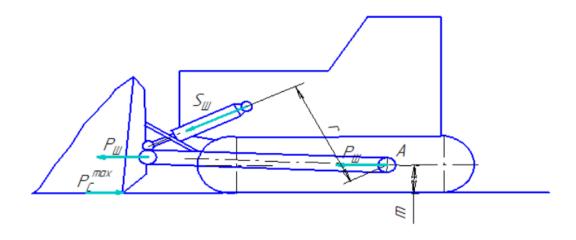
Схема нагрузок в шарнирах рабочего органа
